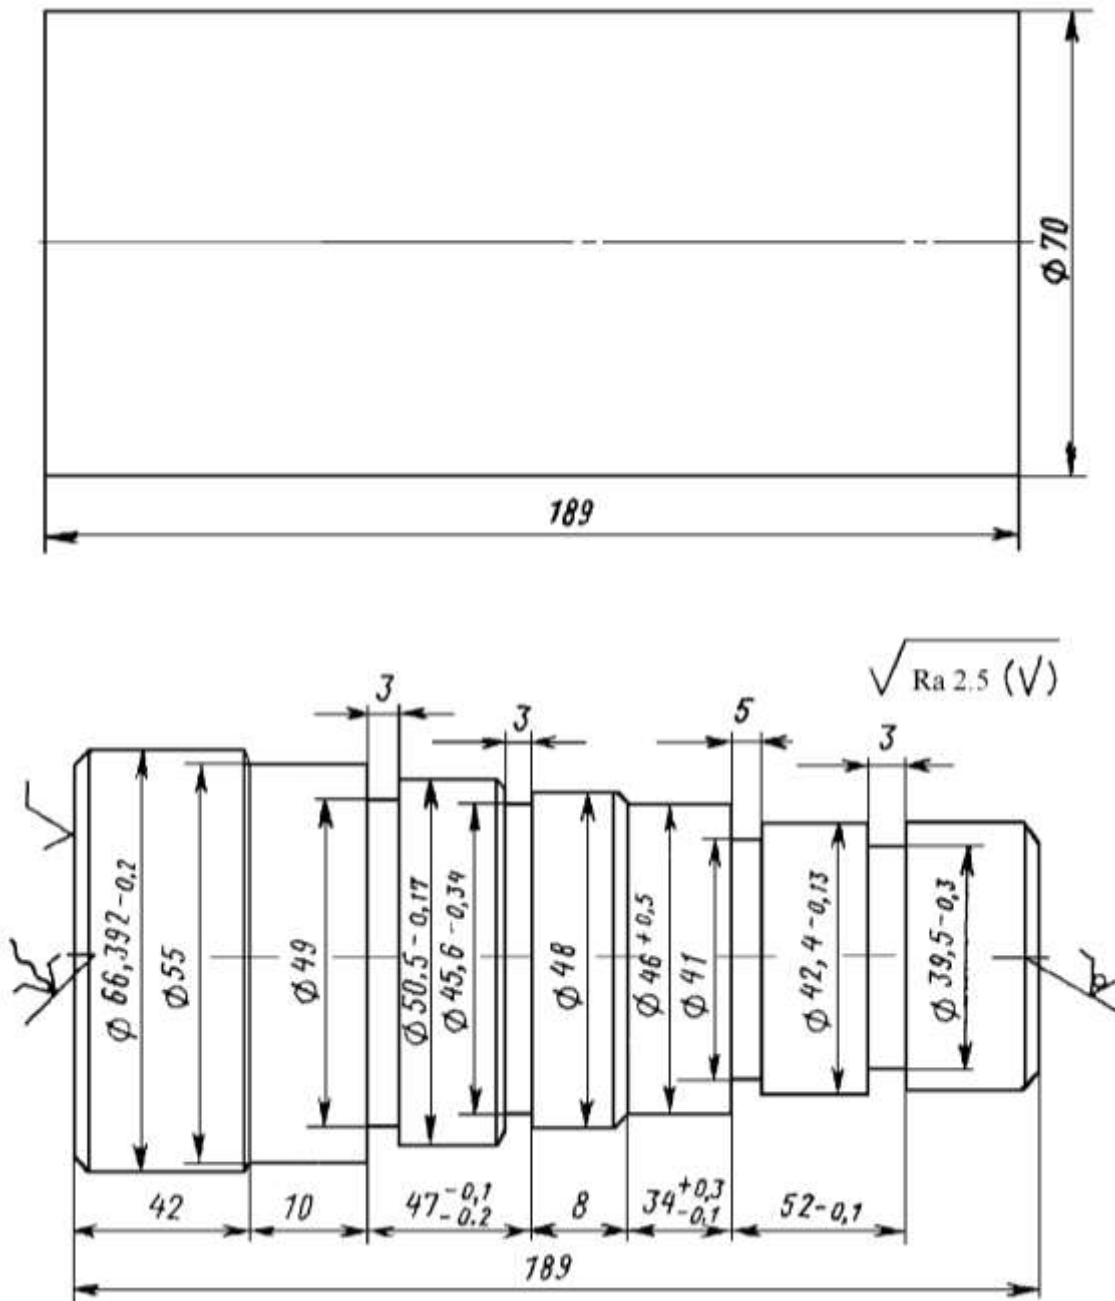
Эскиз заготовки и детали после первой операции технологического процесса изготовления вала-шестерни
